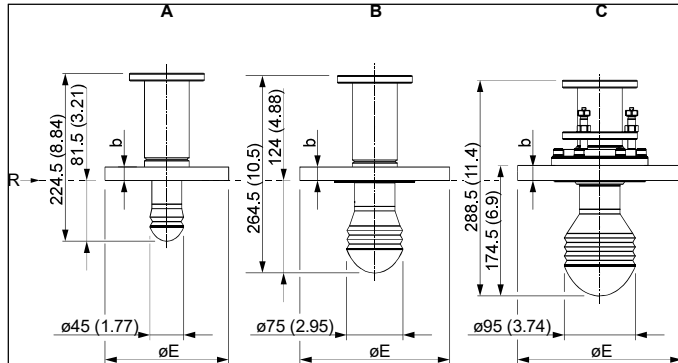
Maßblatt Antennenbaugruppen NMR81
